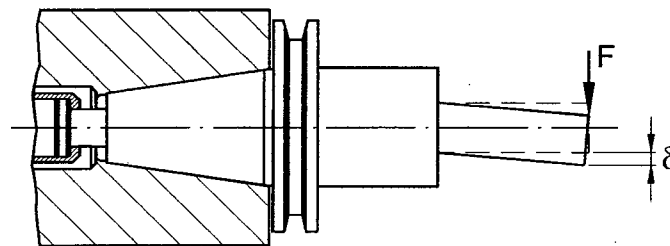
Deflexão da fresa de topo causada pela força de usinagem [16]
